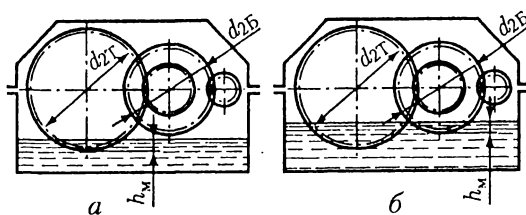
Смазывание передач цилиндрического двухступенчатого зубчатого редуктора [3]:
